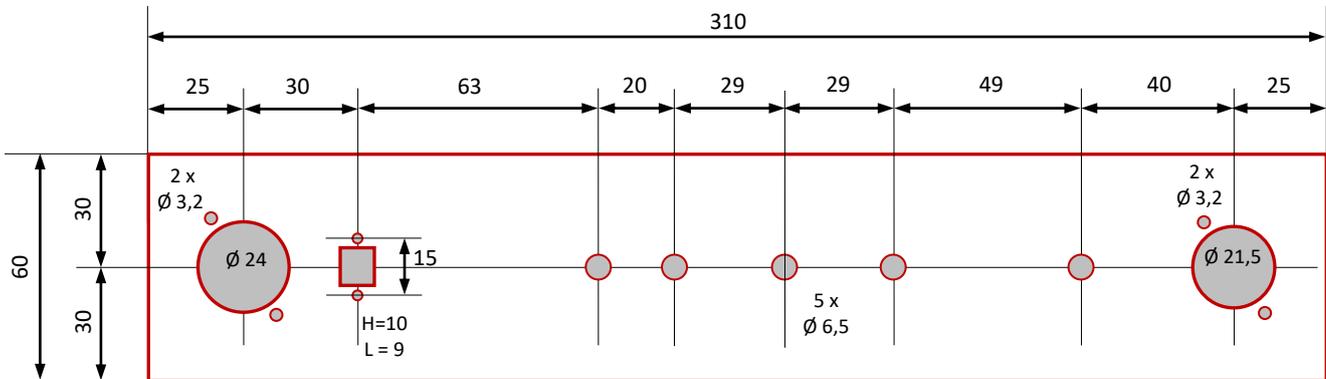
plan de l'usinage de la face arrière – Échelle ½
